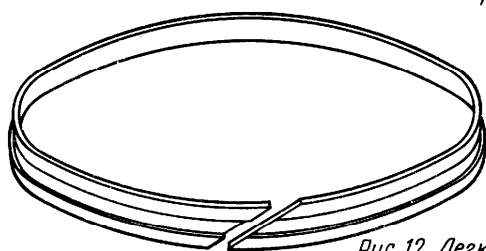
Легкое подкладное кольцо для сварки кольцевых швов
